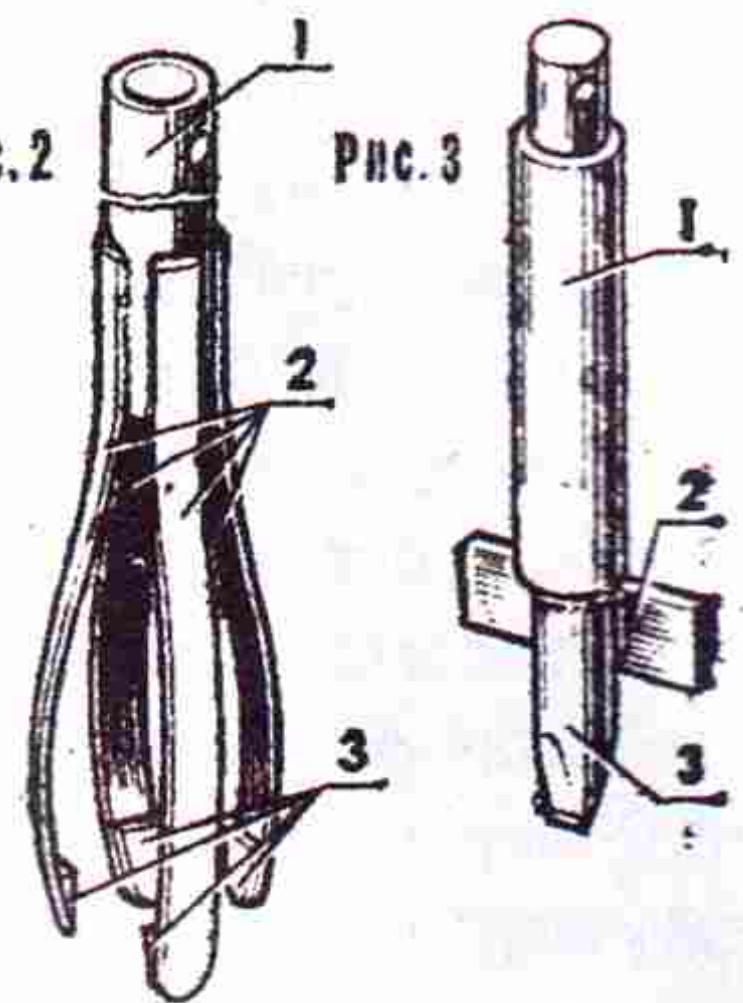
Подрібнювач камення: 1— стержень; 2— поздовжній ніж; 3— зубило.
